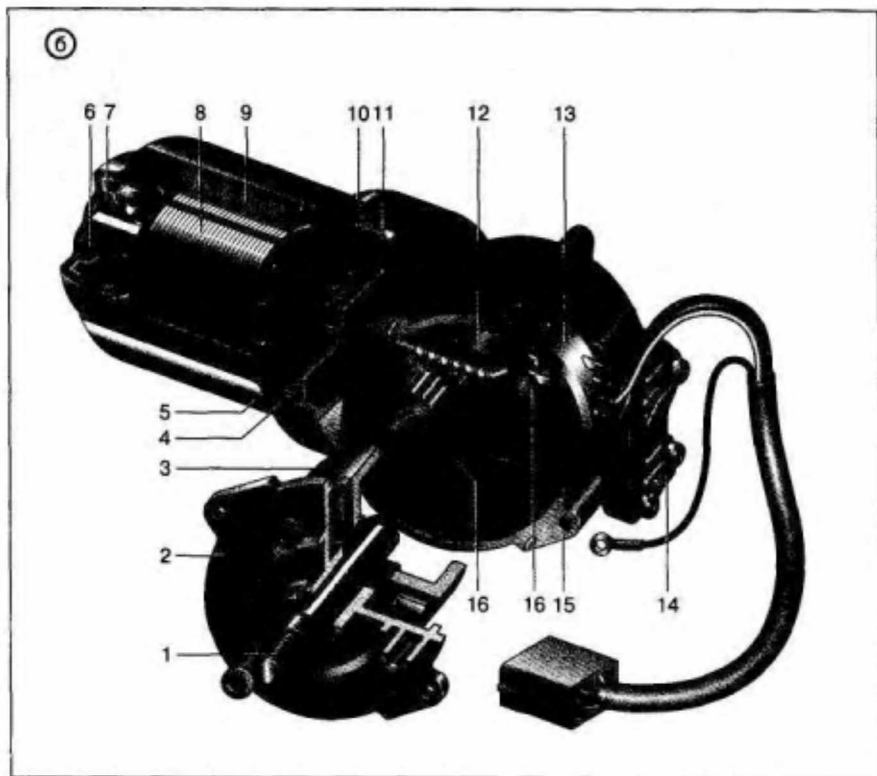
б. Электродвигатель стеклоочистителя: 1 — выходной вал мотор-редуктора; 2 — крышка; 3 — ведомая шестерня; 4 — щеткодержатель; 5 — корпус; 6 — втулка вала якоря; 7 — войлочное кольцо; 8 — якорь; 9 — постоянный магнит; 10 — пластина крепления редуктора; 11 — траверса; 12 — промежуточная шестерня; 13 — колодка с контактами концевого выключателя; 14 — термовиметаллический предохранитель; 15 — картер редуктора; 16 — блок шестерен
